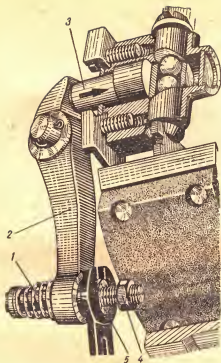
Регулировка привода ручного тормоза автомобиля ГАЗ-51А:
